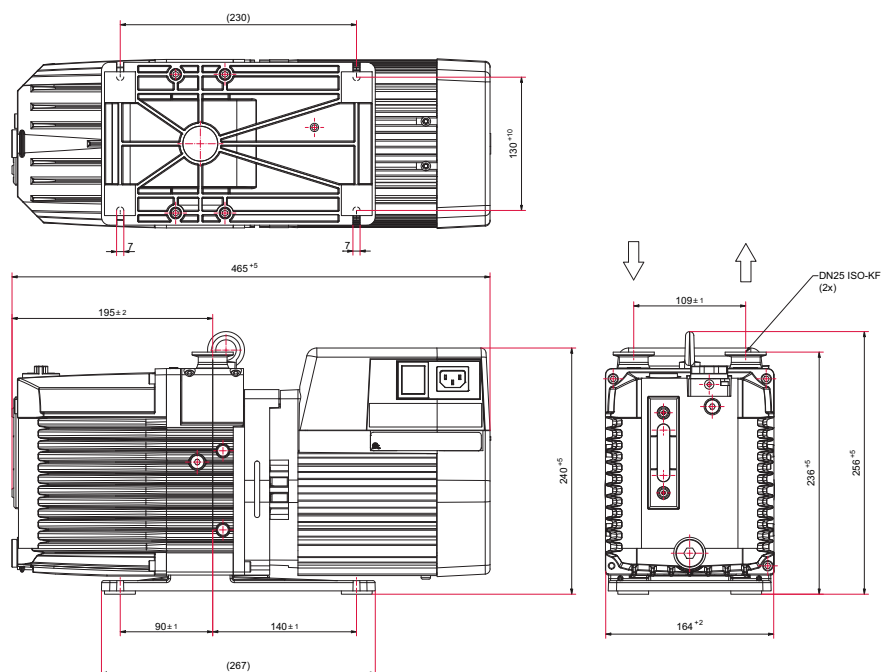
Dimensions DuoVane 18 avec moteur monophasé
